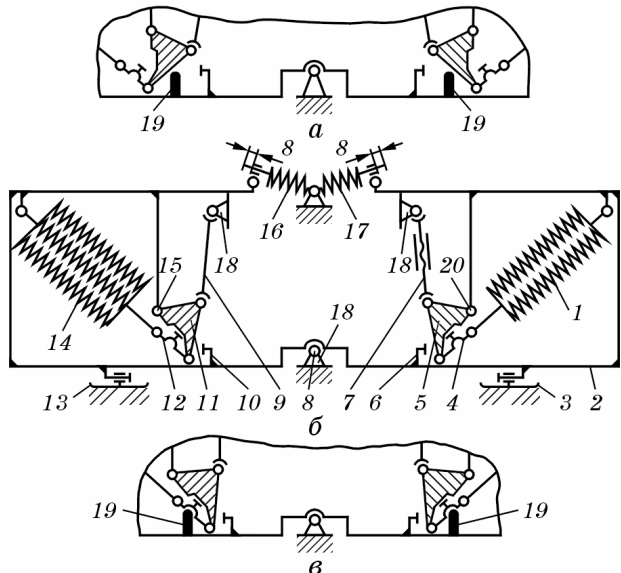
Положення механізму зрівноважування жатки комбайна КЗС-9-1 під час роботи:
